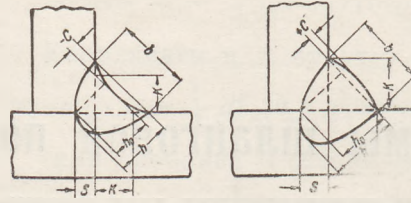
Элементы условных швов, выполненных автоматической и полуавтоматической сваркой:
